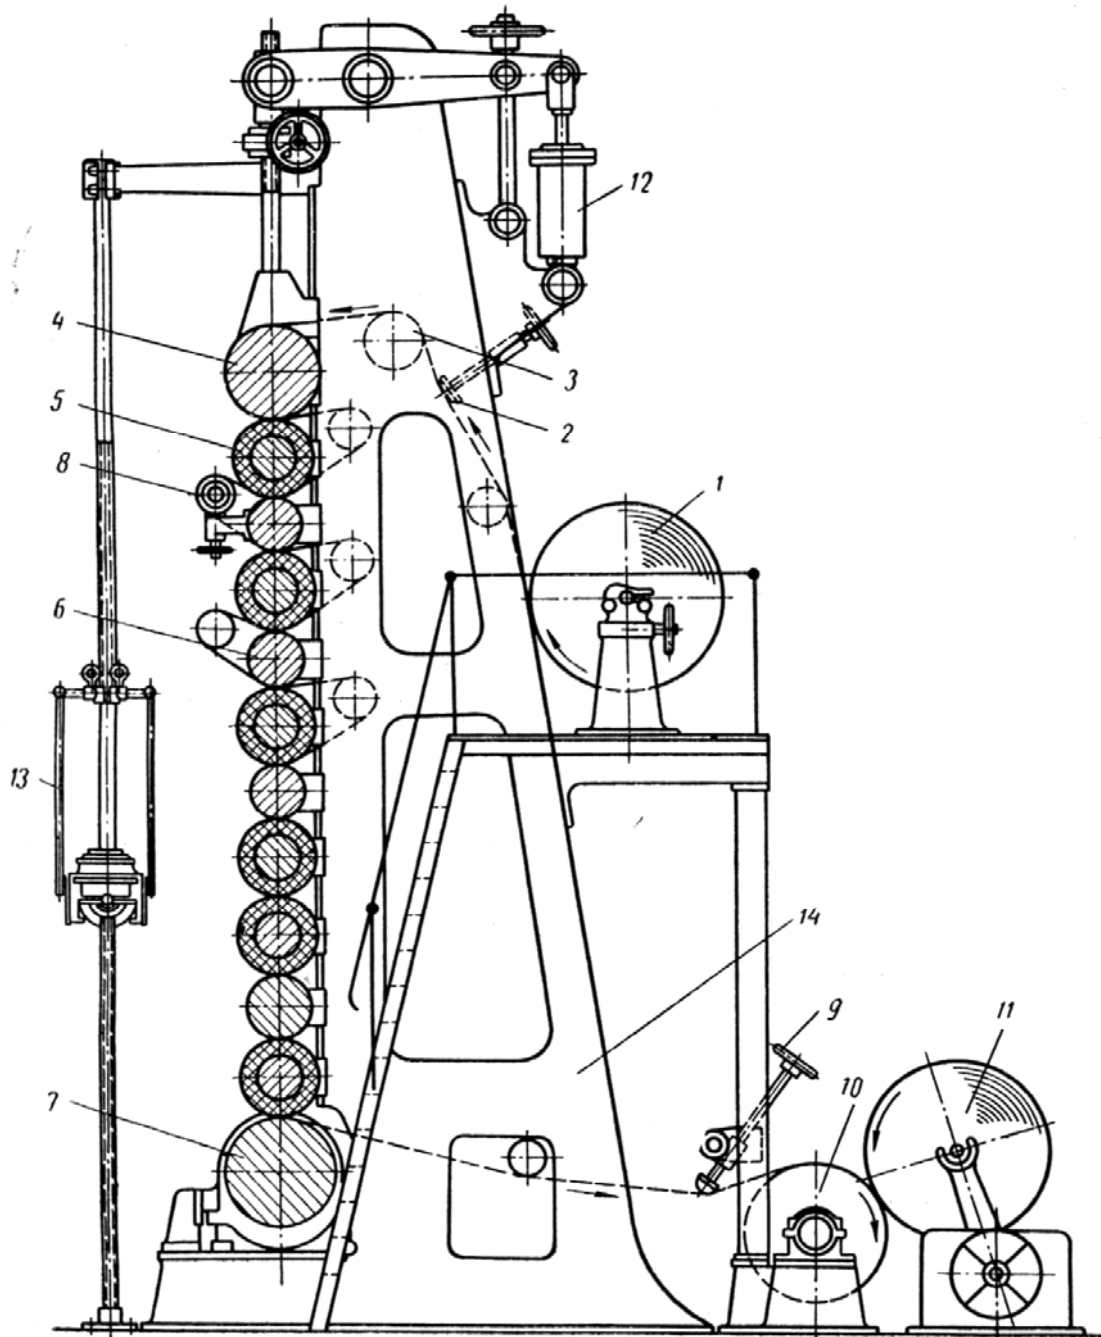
Схема каландру: 1 – розмотувальний рулон; 2 – напрямна дуга; 3 – розгінний валик; 4 – верхній вал; 5 – набивний вал; 6 – металевий вал; 7 – нижній вал; 8 – бумаговедучий валик; 9 – розпрямна дуга; 10 – накат; 11 – намотувальний рулон; 12 – механізм притиску й підйому валів; 13 – підйомник для заправки паперу; 14 – станина каландра
